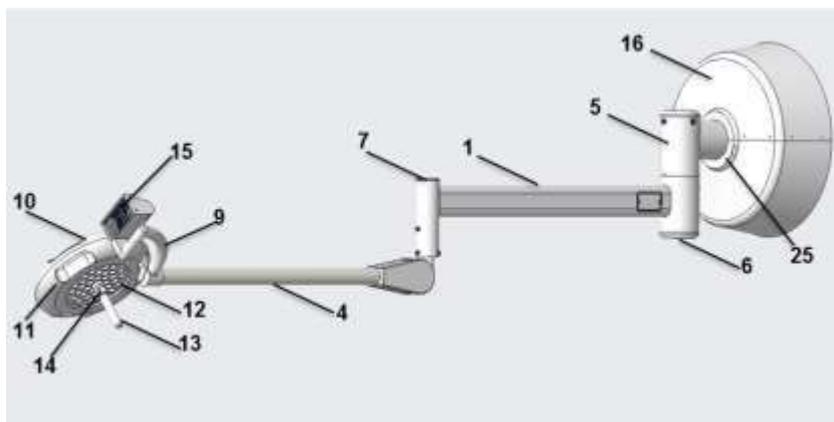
PARTES DO EQUIPAMENTO DE PAREDE SL-300
